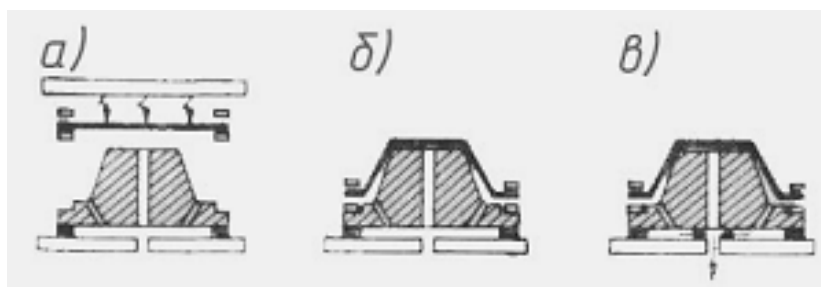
Схема позитивного формування з попередньою механічною витяжкою
